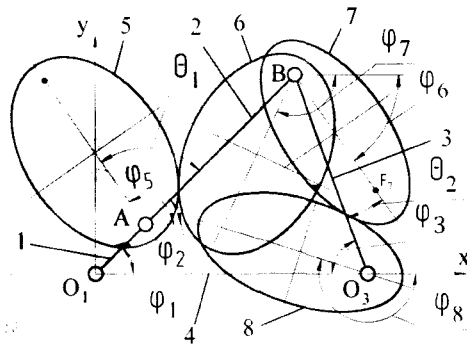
Схема зубчато-рычажного механизма периодического движения на основе эллиптических зубчатых колес
